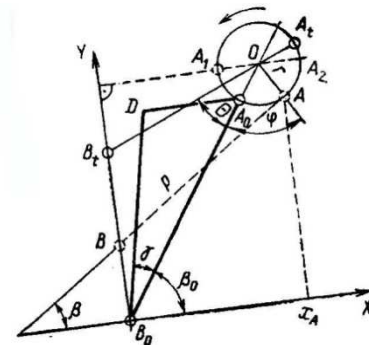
Кінематична схема щоквої дробарки із складним рухом щоки.
